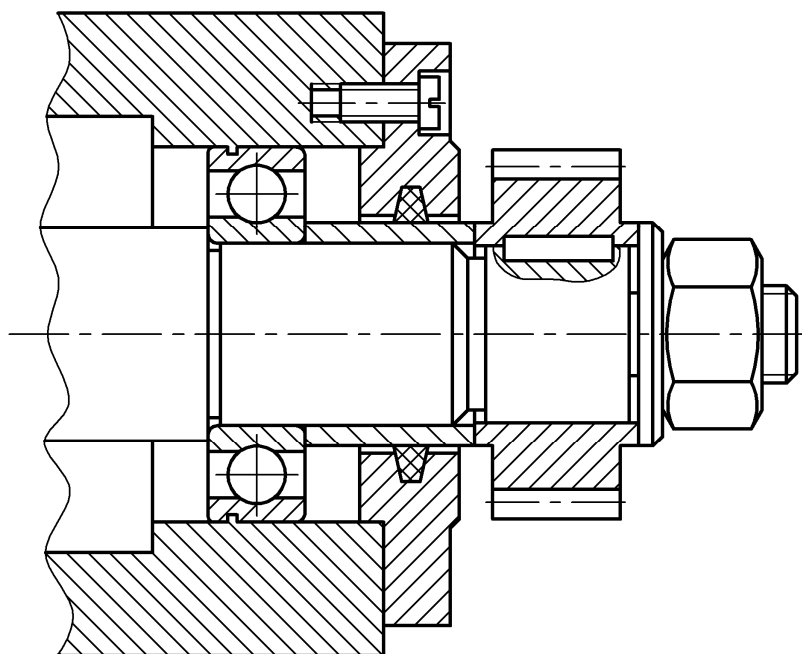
Пример нанесения штриховки смежных деталей на сборочном чертеже. Вал, шпонка, винт, гайка, шайба на разрезе изображаются как на виде
